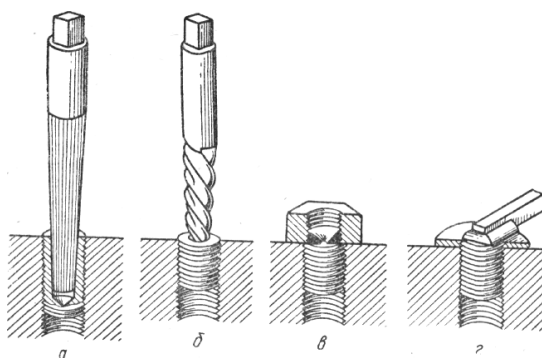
Інструменти і прийоми для викручування зламаних шпильок і болтів: а – бор, б — екстрактор, в — приварювання гайки; г — приварювання дроту
